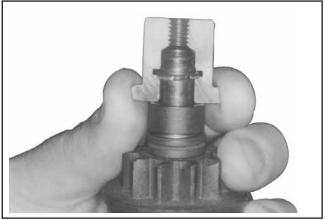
Innere Hälfte des Werkzeugs um Ankerwelle und Haltering befestigen.
